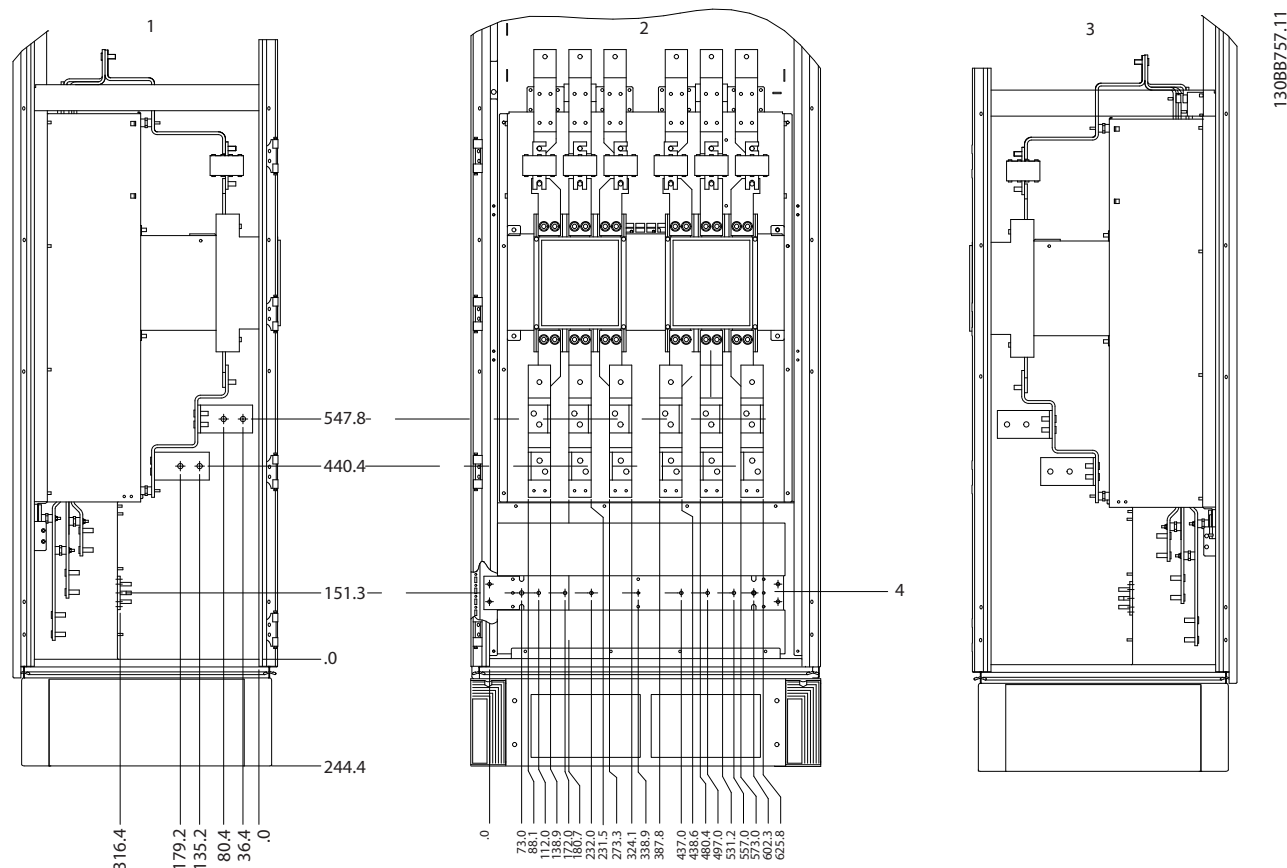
Расположение клемм — шкаф дополнительных устройств, корпус размера F9
